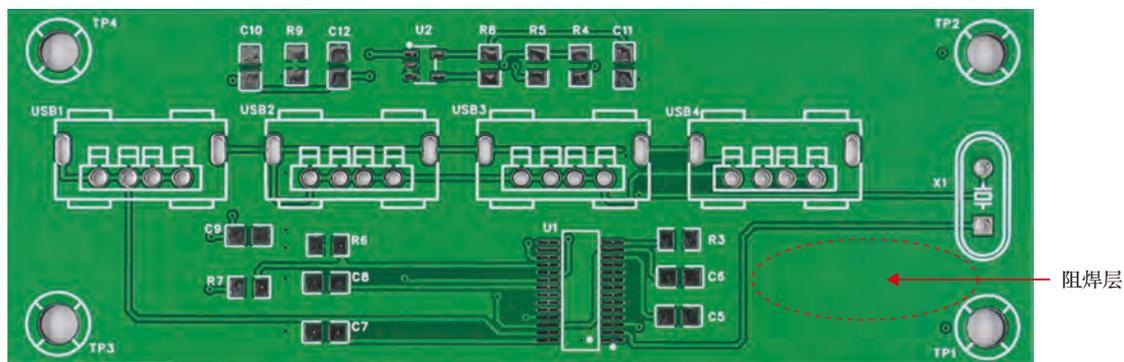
PCB 实物上的阻焊层（油墨覆盖区域）
